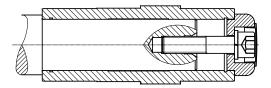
Крепление редуктора к валу с упором с помощью крепежного узла
